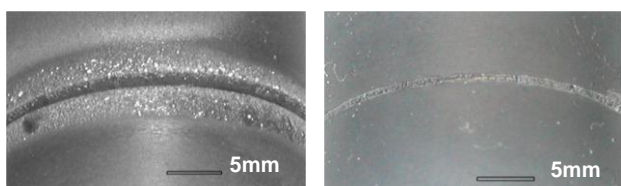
Foto gelöteter Kapseln (links: Nd:YAG- Laser bearbeitet, rechts: CO₂- Laser bearbeitet)
